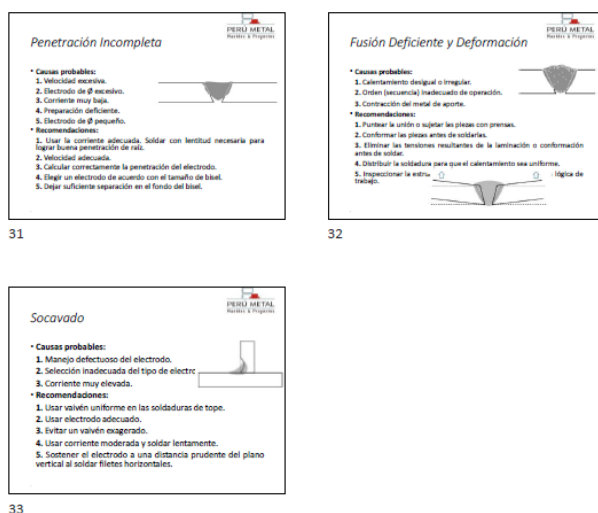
Láminas 31-33 de capacitación sobre técnicas de soldadura
